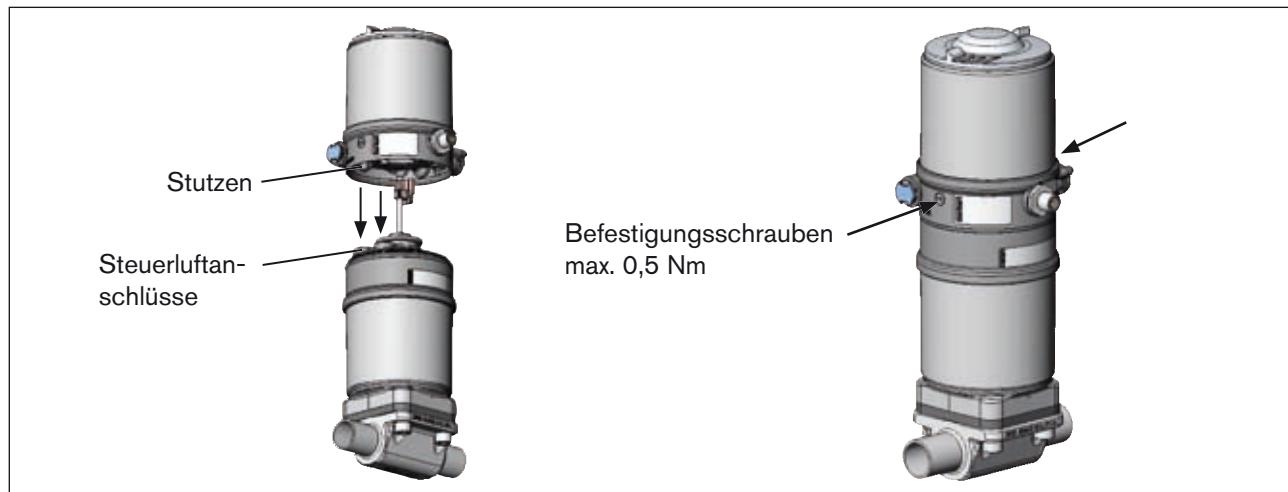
Montage Positioner, Reihe 2103, 2300 und 2301
